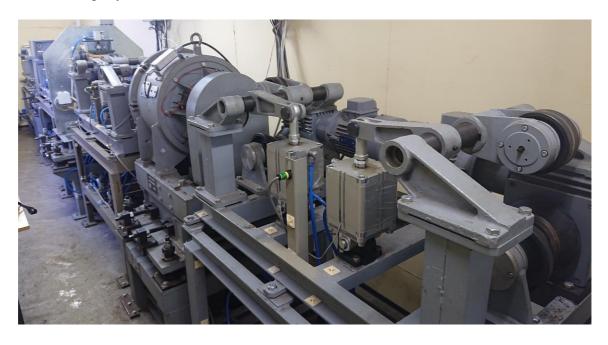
Общий вид установок неразрушающего контроля насосно-компрессорных труб
